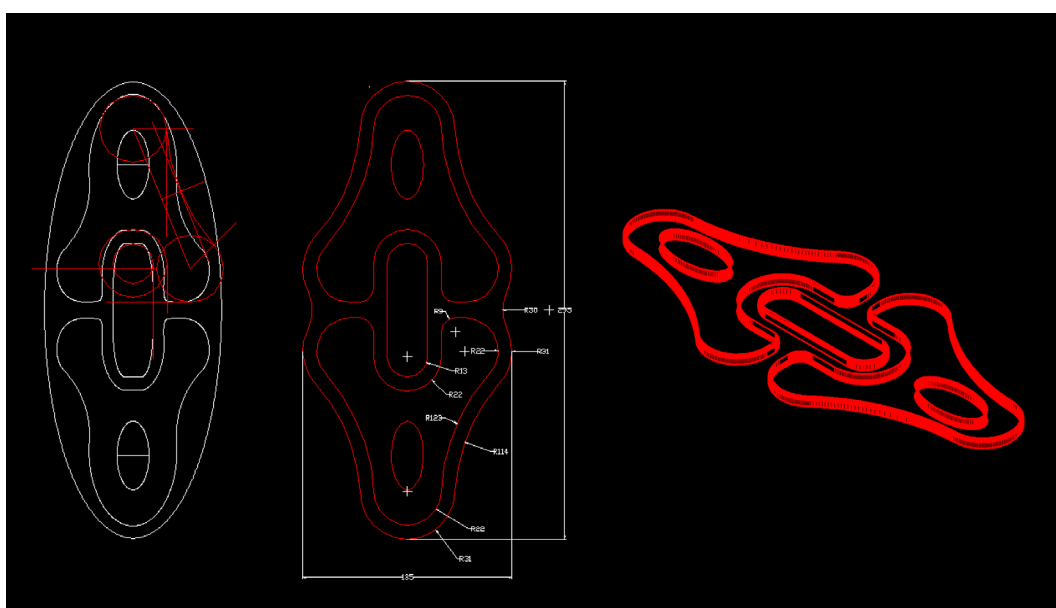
Desenho CAD com a geometria do pad de proteção planificado.
